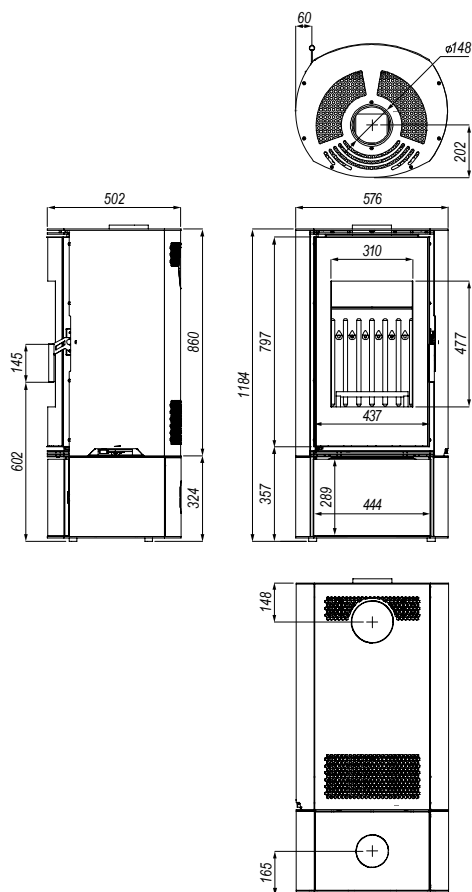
Wymiary (w mm) pieca wolnostojącego serii IGNIS w wersji SOLUM BOX.
